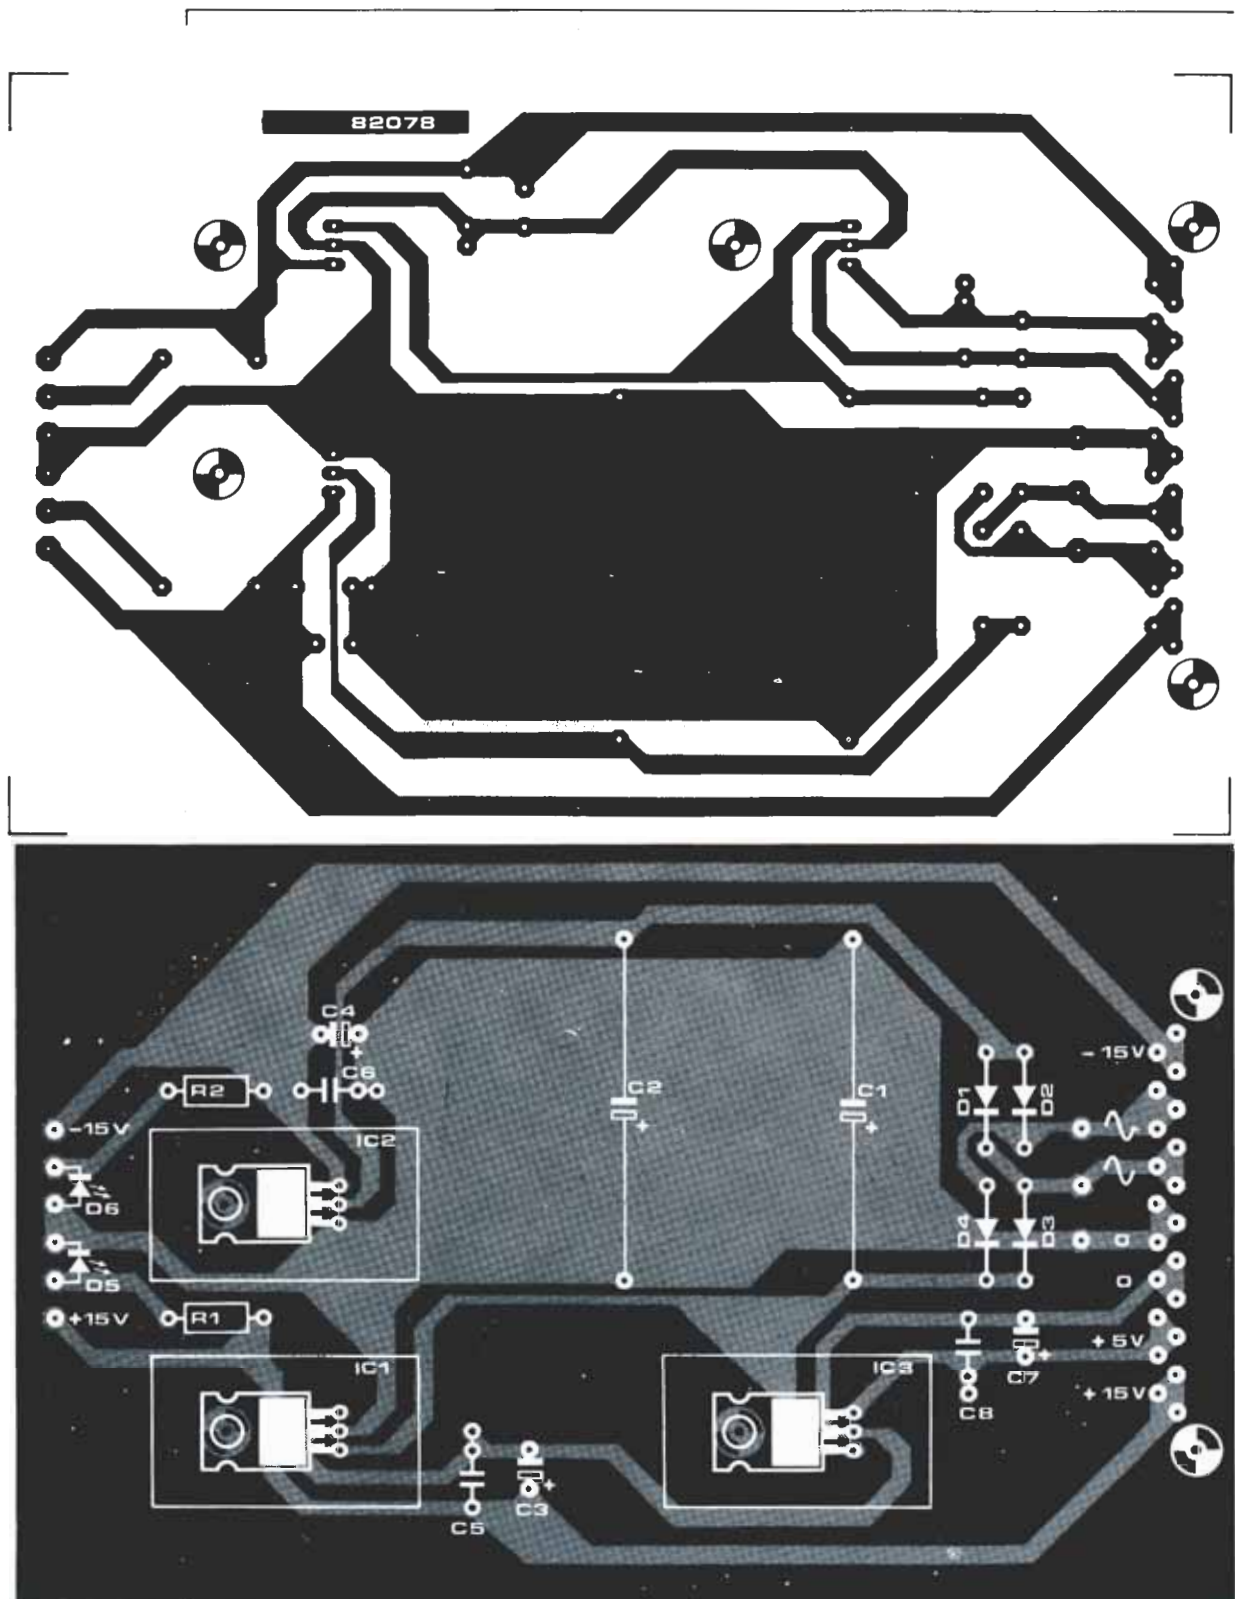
Placa de circuito impreso y disposición de los componentes de la fuente de alimentación.
